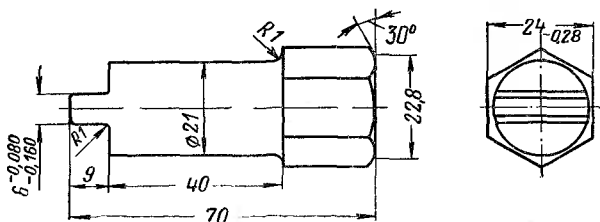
Головка ключа для затяжки гайки крепления автоматической муфты
